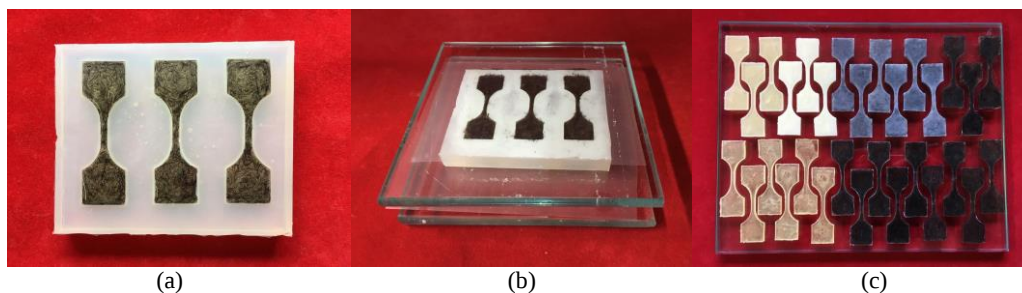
Etapas de moldagem dos corpos de prova: (a) moldagem em molde de silicone; (b) confinamento para cura inicial; (c) peças confinadas entre placas de vidro para cura final
